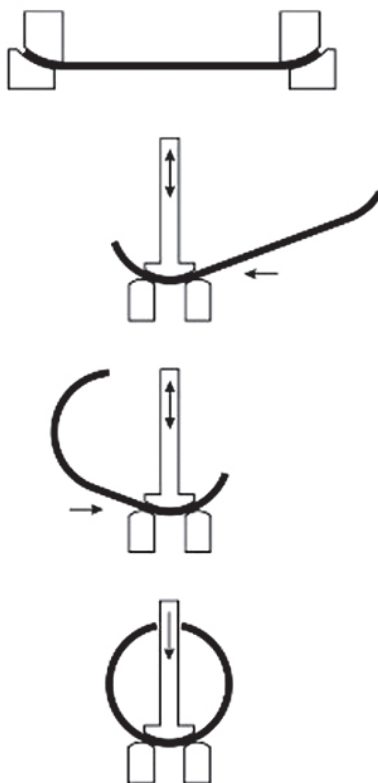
Схема постепенной формовки трубной заготовки штампами
